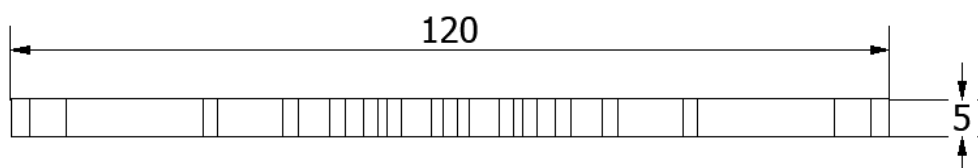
Acotamiento de la placa. Vista lateral. Representación de dimensiones en milímetros.
